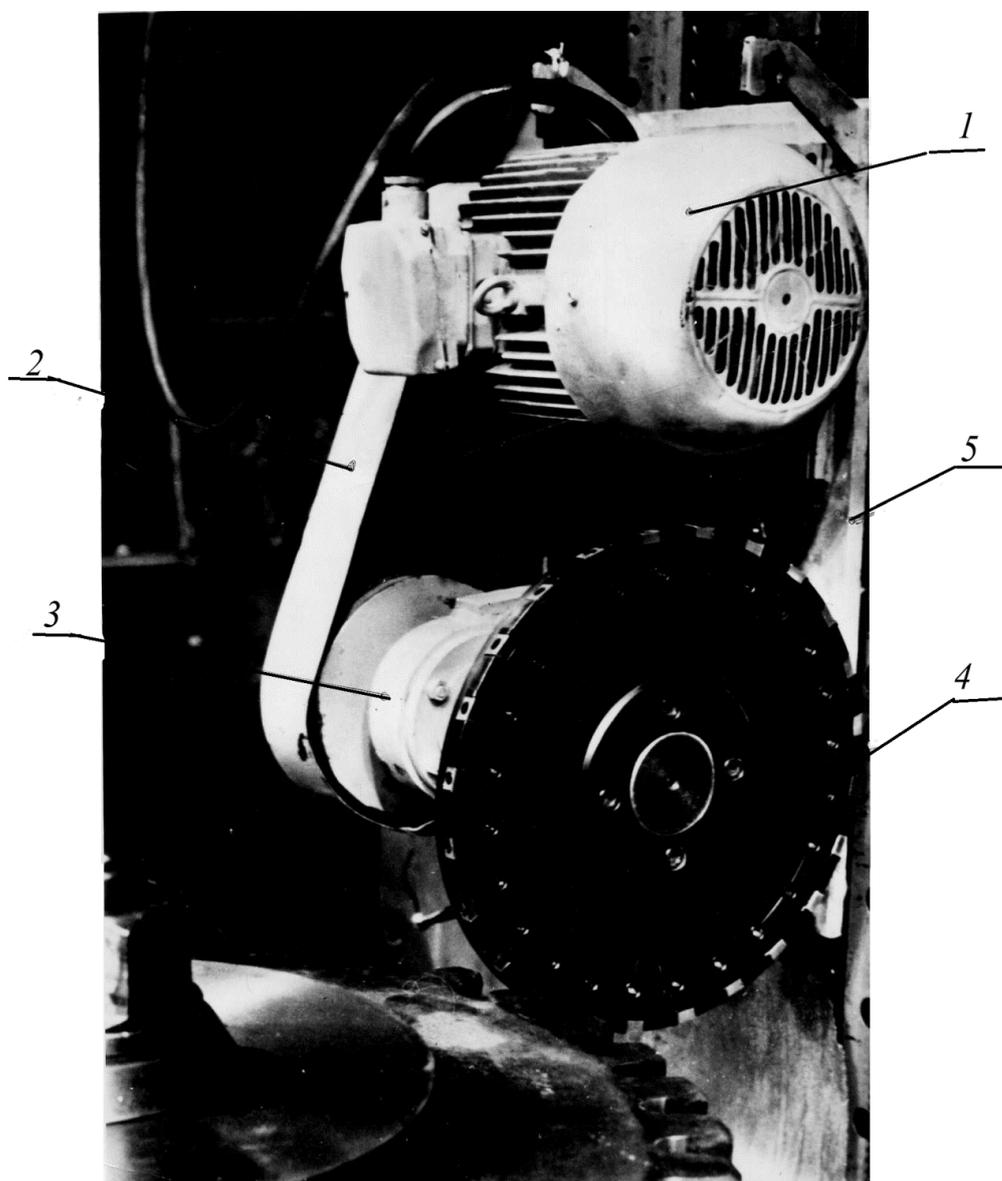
Рабочая конструкция спецсуппорта к зубострогальному станку фирмы "МАОГ":
